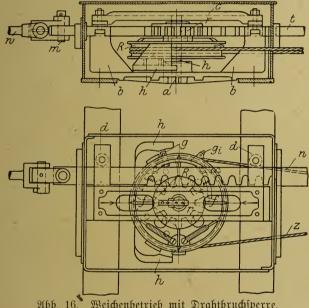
Beichenbetrieb mit Drahtbruchsperre.
